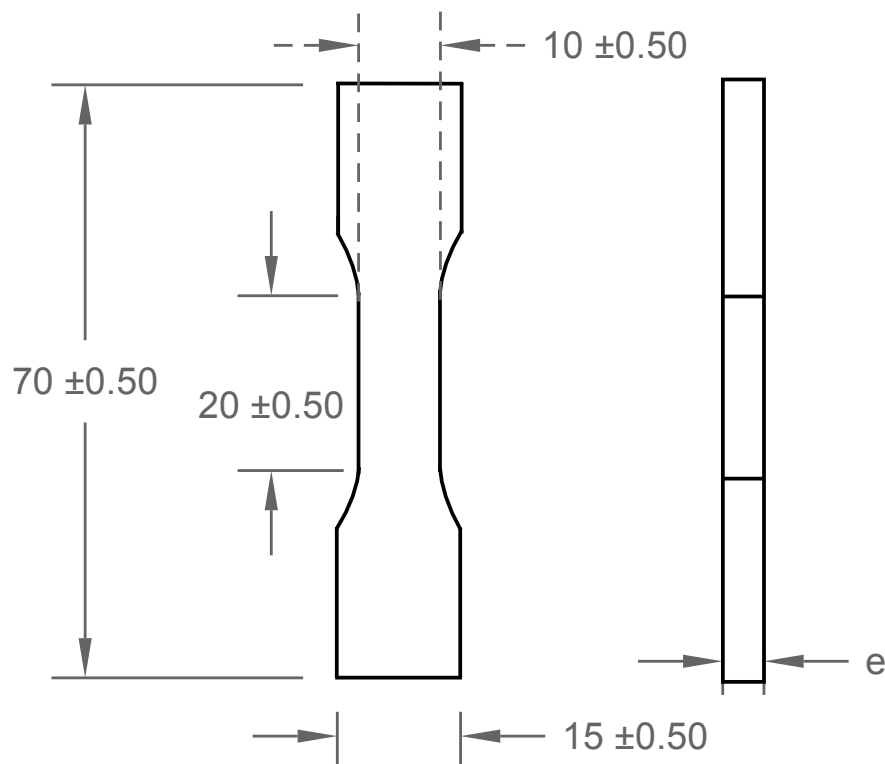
Dimensions des éprouvettes utilisées pour cette étude.
